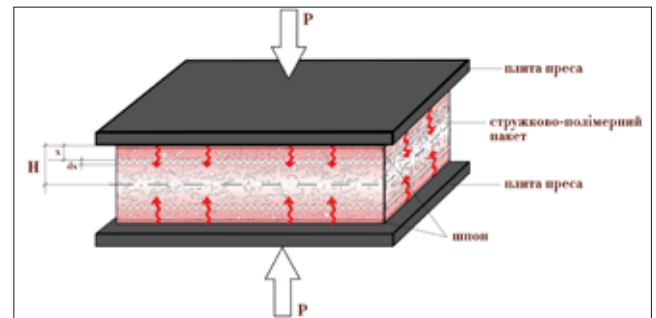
Схематичне зображення стружково-полімерного пакета між плитами преса
